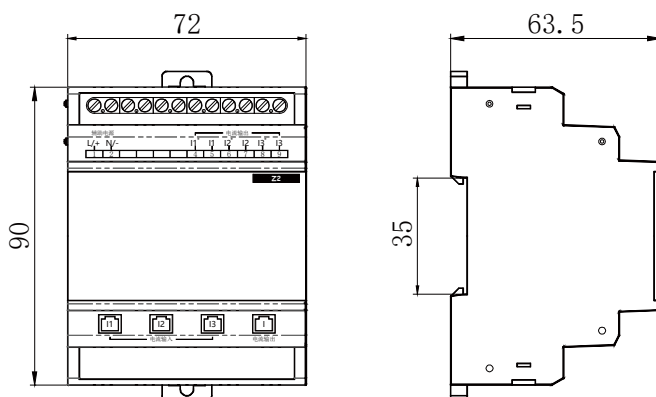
Внешний вид и габаритные размеры модуля коммутации Z2
